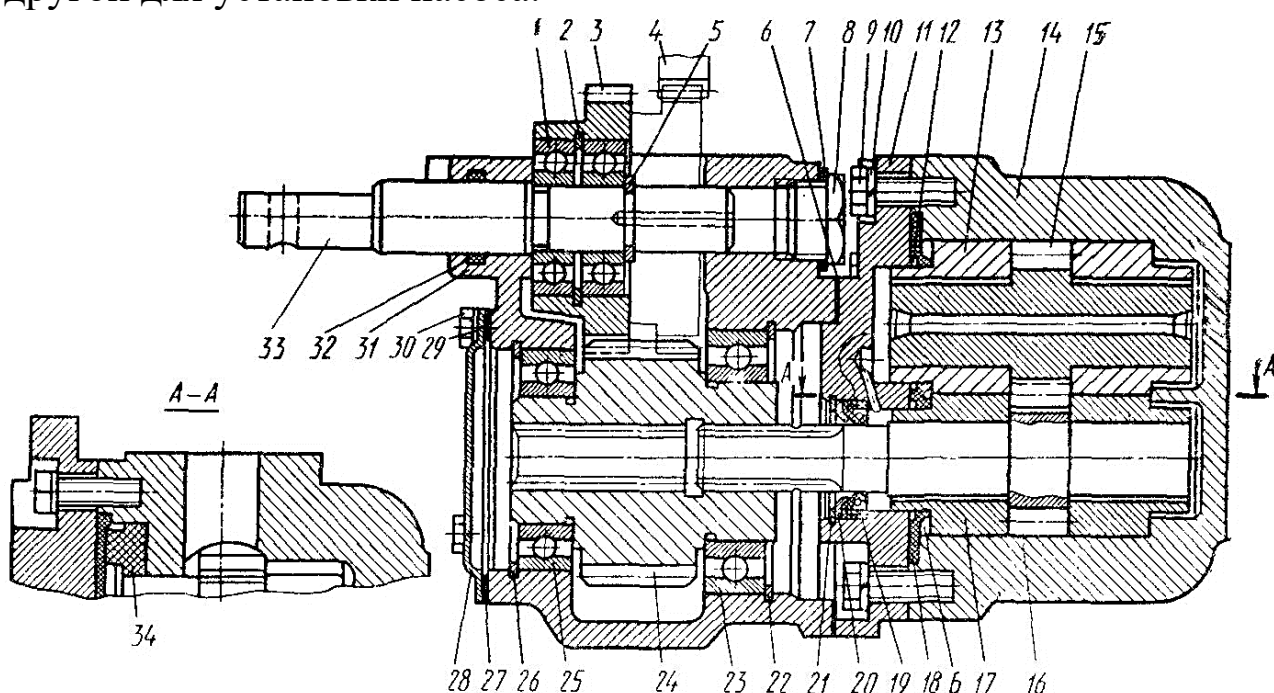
Коробка отбора мощности и насос самосвала ЗИЛ: 1 – шариковые радиальные подшипники; 2, 5, 22, 26 – стопорные кольца; 3, 4, 16, 24 – шестерни; 6 – картонные прокладки; 8 – пробка с алюминиевой прокладкой; 9 – болт; 10 – пружинные шайбы; 11, 28 – крышка; 12 – кольцо; 13, 17 – втулки; 14 – корпус насоса; 15 – колесо; 18 – манжета; 19 – армированная манжета; 20 – кольцо упорное; 21 – кольцо стопорное; 23, 25 – радиальные подшипники; 24 – колесо; 27 – прокладка; 29 – пружинные шайбы; 30 – болт; 31 – картер; 32 – уплотнительное кольцо; 33 – ось; 34 – уплотнение
